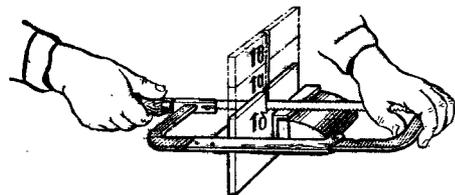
Приемы резания металла ручной слесарной ножовкой с поворотом ножовочного полотна
